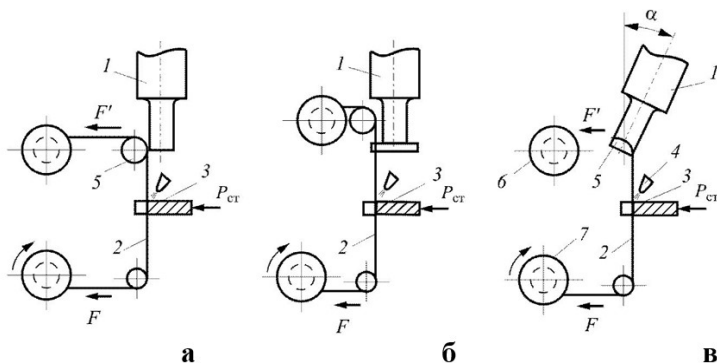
Принципиальные схемы ультразвуковой размерной обработки непрофилированным инструментом: 1 – концентратор; 2 – инструмент-проволока; 3 – заготовка; 4 – абразивная суспензия; 5 – шип; 6, 7 – катушка
